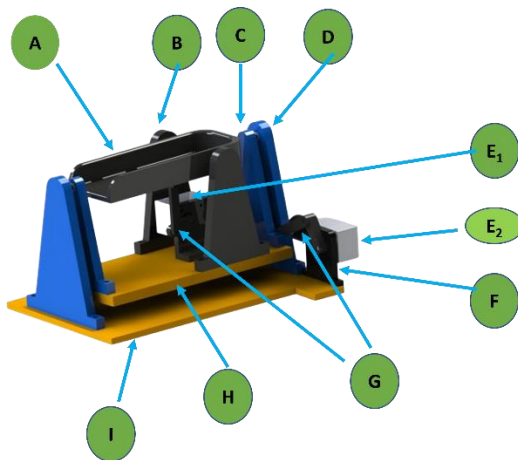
Componentes del rehabilitador de tobillo. A) Base móvil, B) Soporte D/P, C) Soporte I/E, D) Soporte fijo, E) Motorreductores, F) Base motor, G) Mecanismo de 4 barras, H) Base secundaria, I) Base principal.
